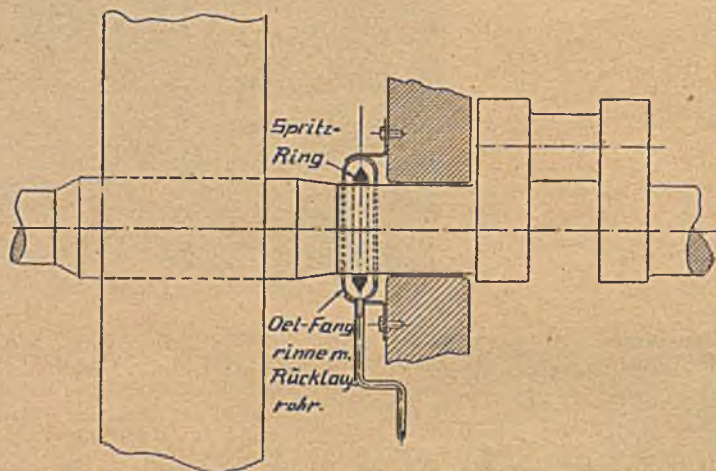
Spritzring mit Ölfangrinne zwischen Hauptlager und Schwungrad
